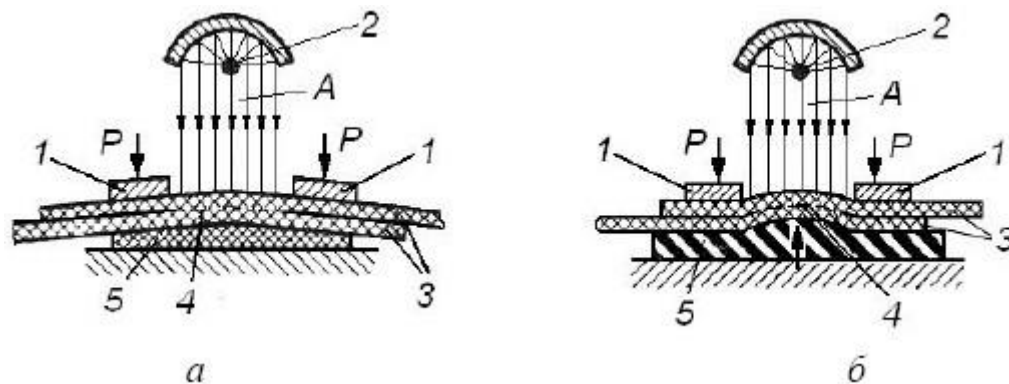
Сварка ИК-излучением: а - на жесткой подложке; б - на упругой подложке; 1 - губки, ограничивающие зону облучения; 2 - нагреватель; 3 - свариваемые пленки; 4 - сварной шов; 5 - подложка; А - ИК-луч; Р - давление прижима
